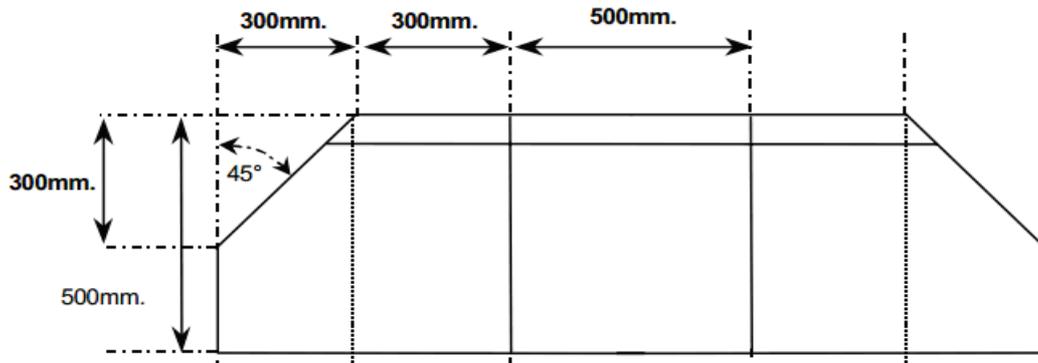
Dimensions de la barrière AE-MDB en vue de dessus
